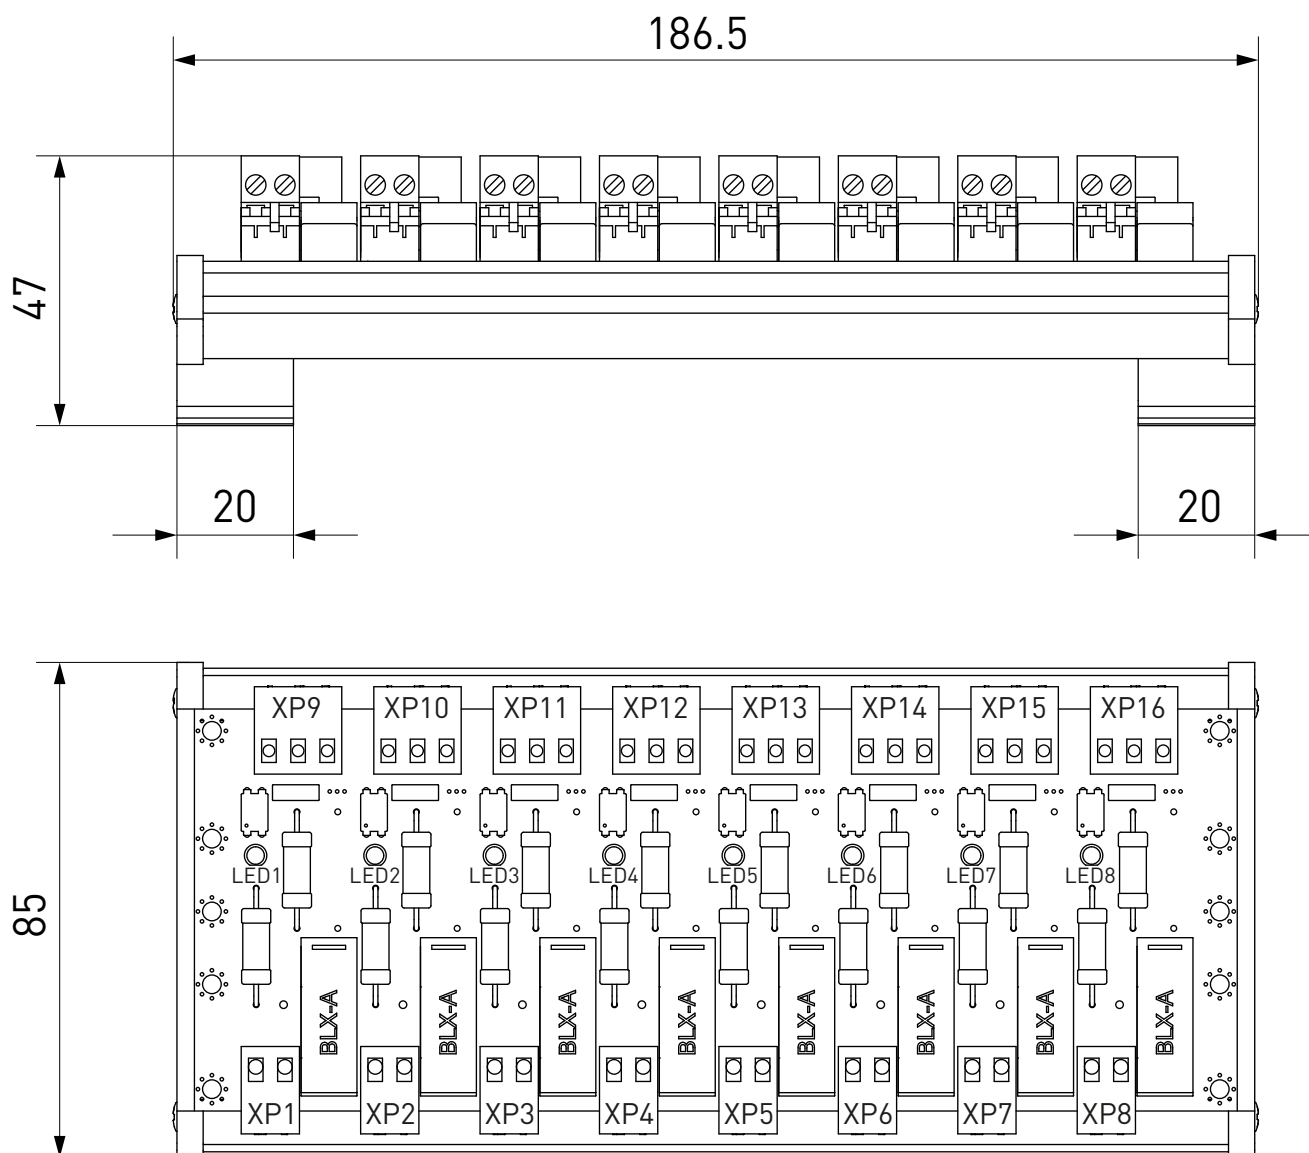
Габаритные размеры блока предохранителей PLP-8F.
